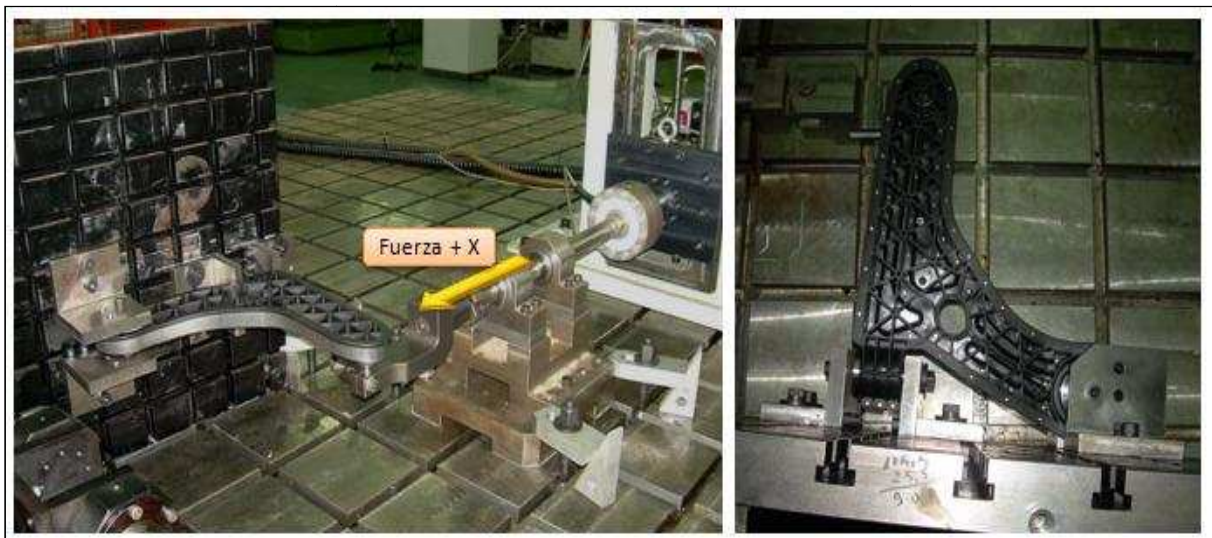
DISPOSICIÓN PARA EL ENSAYO EN LA DIRECCIÓN LONGITUDINAL (EJE X POSITIVO)
